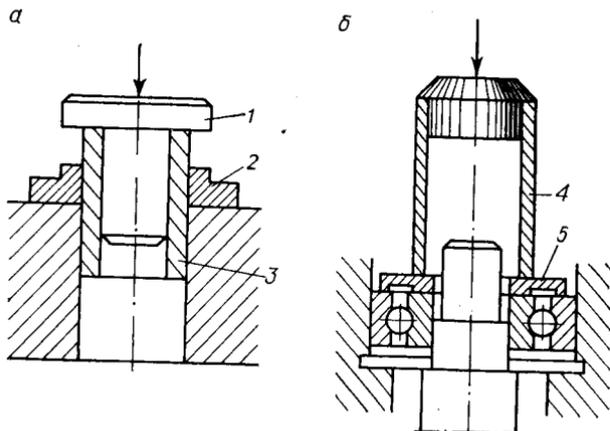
Приспособления для запрессовки втулки (а) и подшипника (б):
